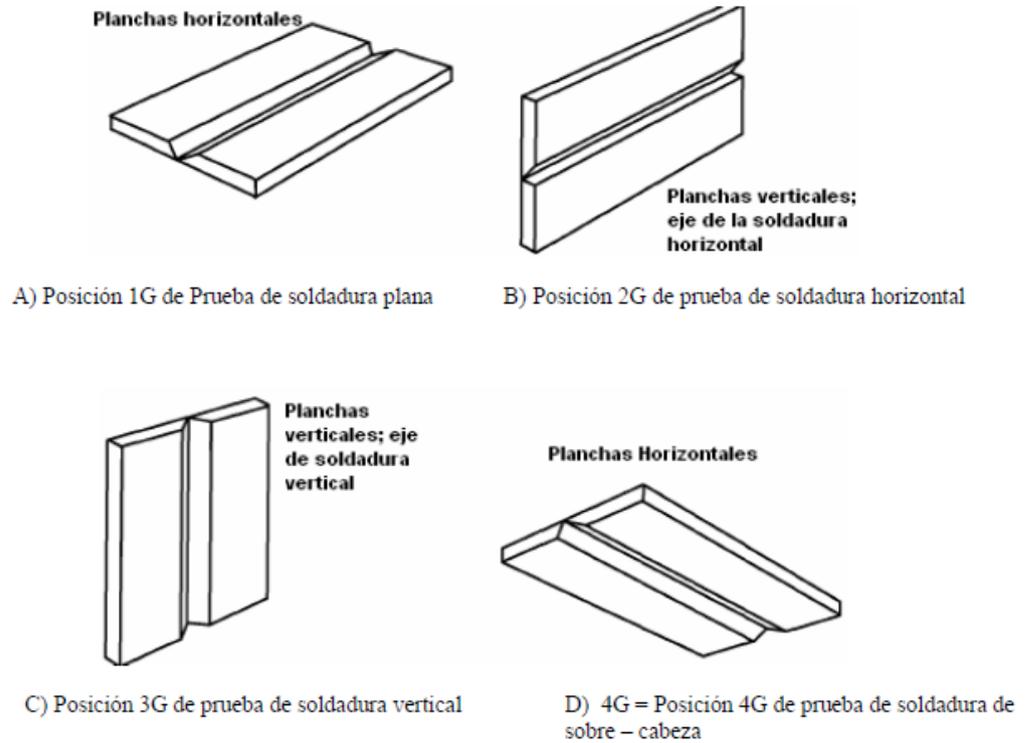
POSICIONES DE PLANCHAS DE PRUEBAS PARA SOLDADURAS DE RANURA. [12]
